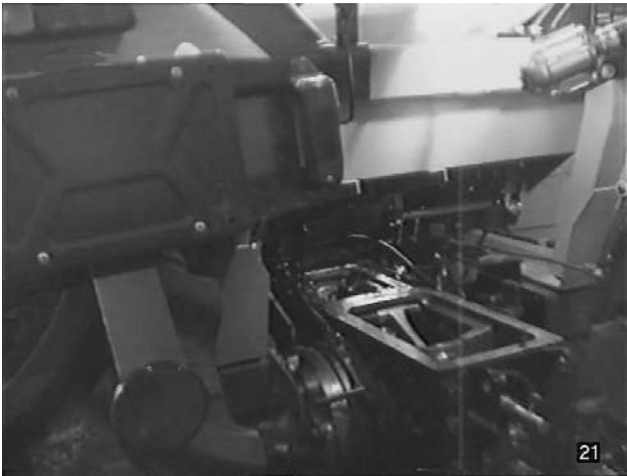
L'accès au démontage de l'embrayage de la P.d.F. arrière est possible sans le dépose de la cabine du tracteur. Désaccoupler les commandes des distributeurs hydrauliques auxiliaires.
